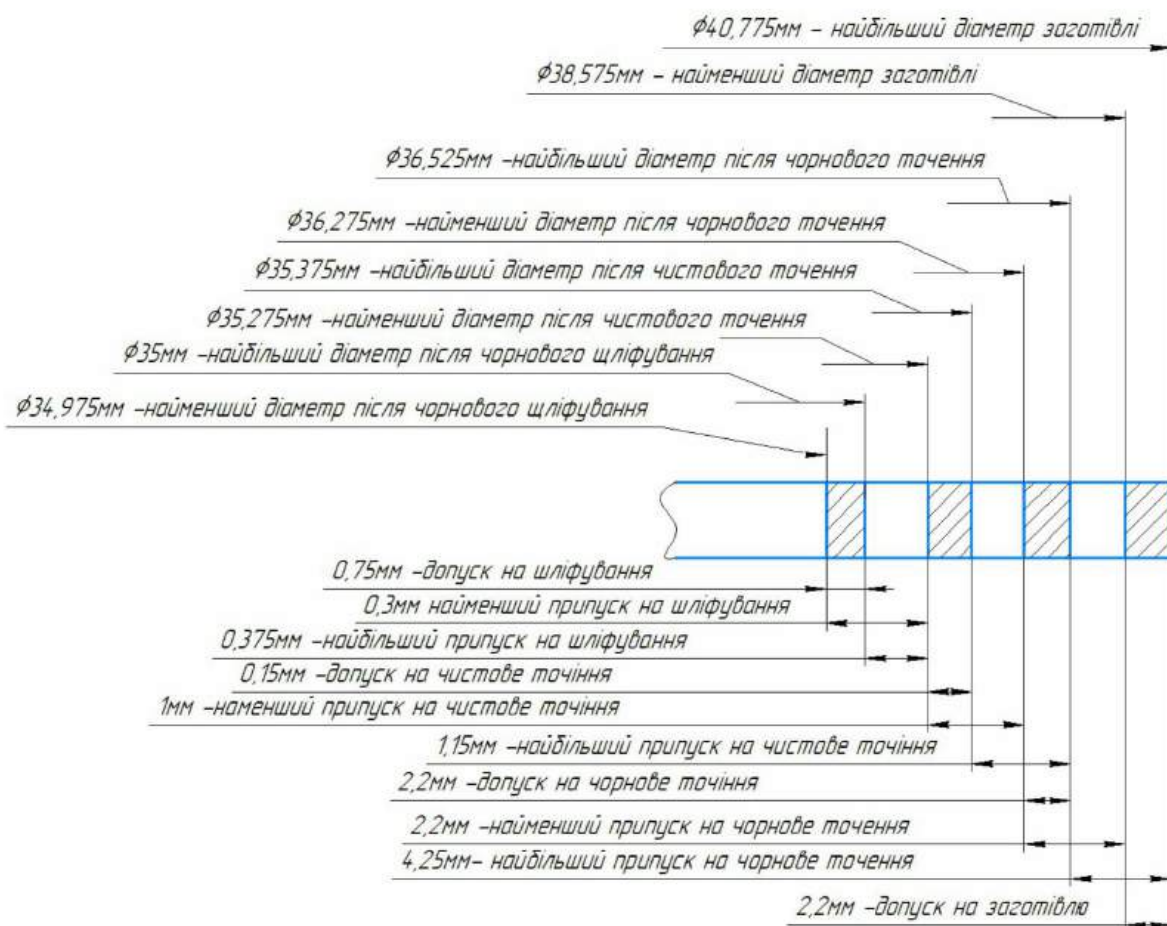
Схема розташування припусків і допусків на обробку поверхні
